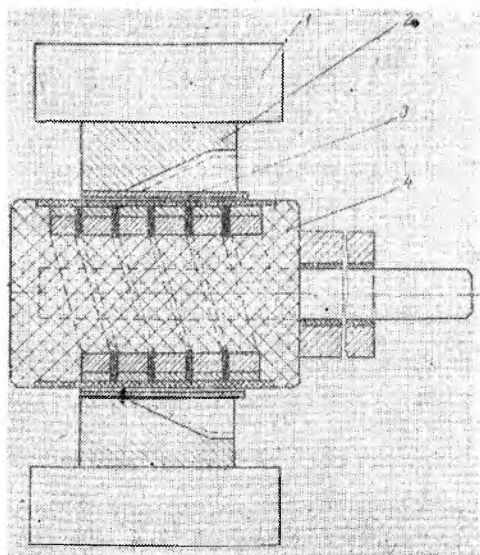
Схема процесса раздачи трубчатых заготовок энергией ИМП
